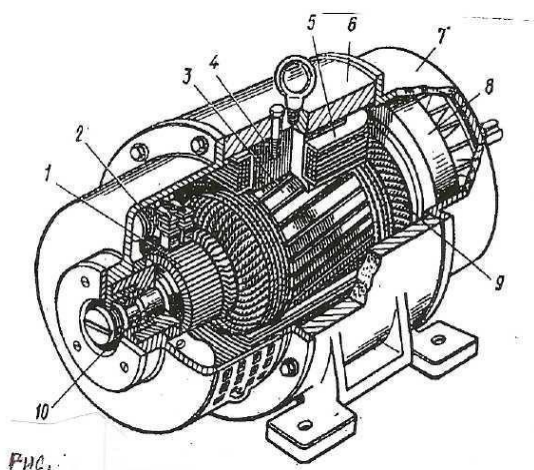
Устройство электрической машины постоянного тока 1- коллектор; 2 – щетки; 3, 9 - сердечник и обмотка якоря; 4 – главный полюс; 6 – катушка обмотки возбуждения; 6 – станина (корпус); 7 – подшипниковый щит; 8 – вентилятор; 10 – вал
